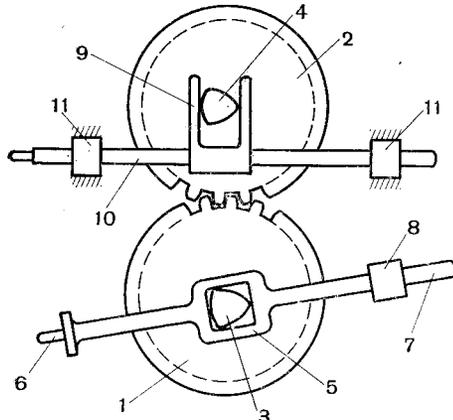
Грейферный механизм кулачкового типа с контргрейфером
